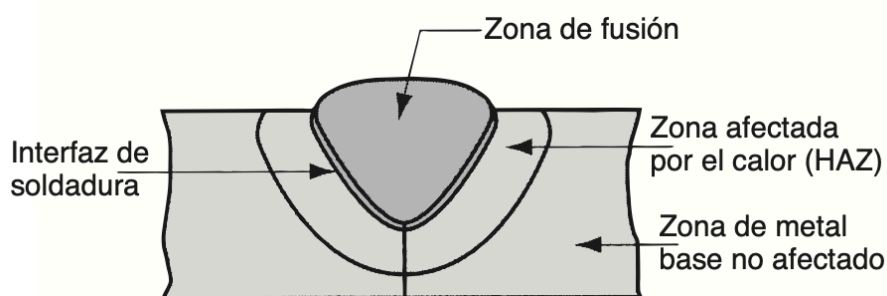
Sección transversal de una soldadura por fusión. [26]
